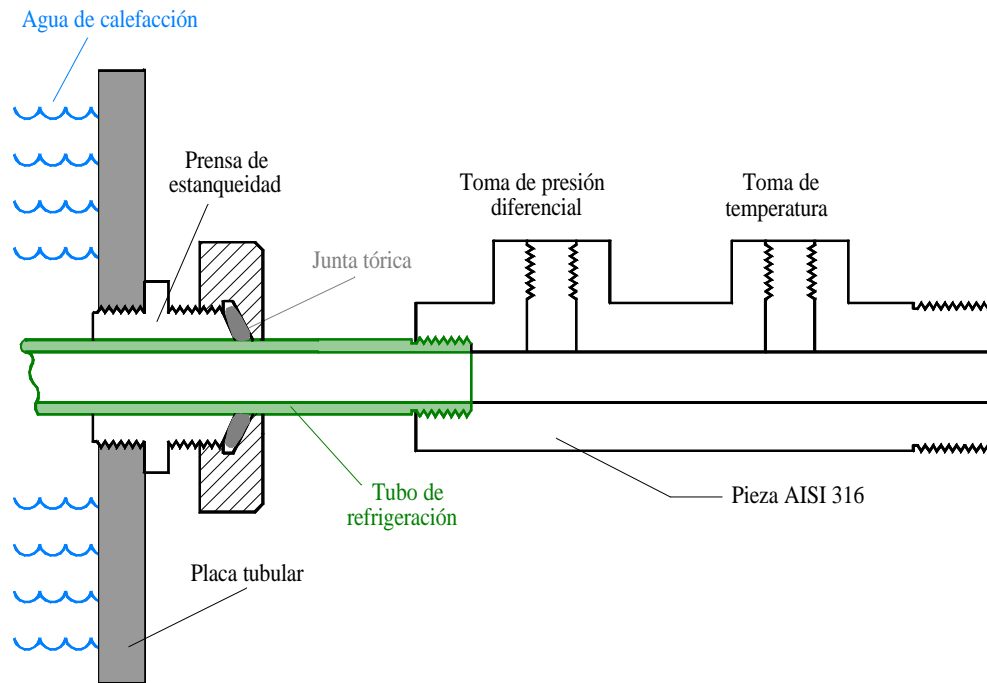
Disposición de un tubo en la placa tubular del intercambiador de calor.
